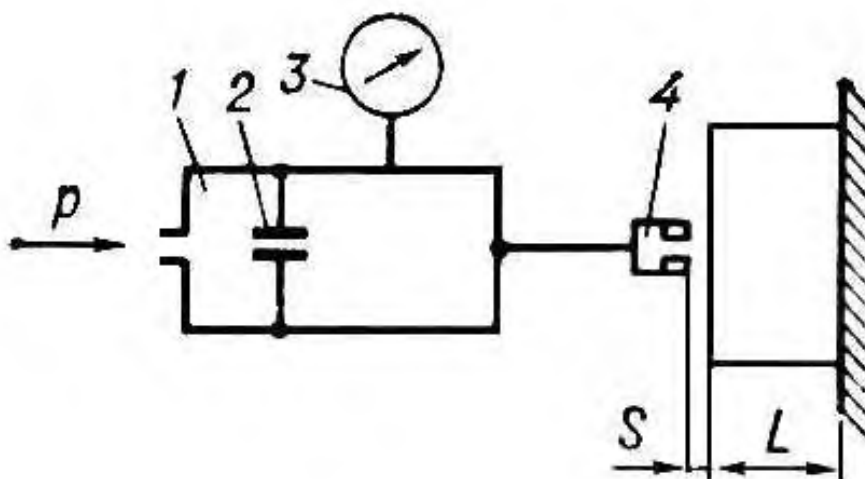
Пневматичний вимірювальний прилад манометричного типу:
